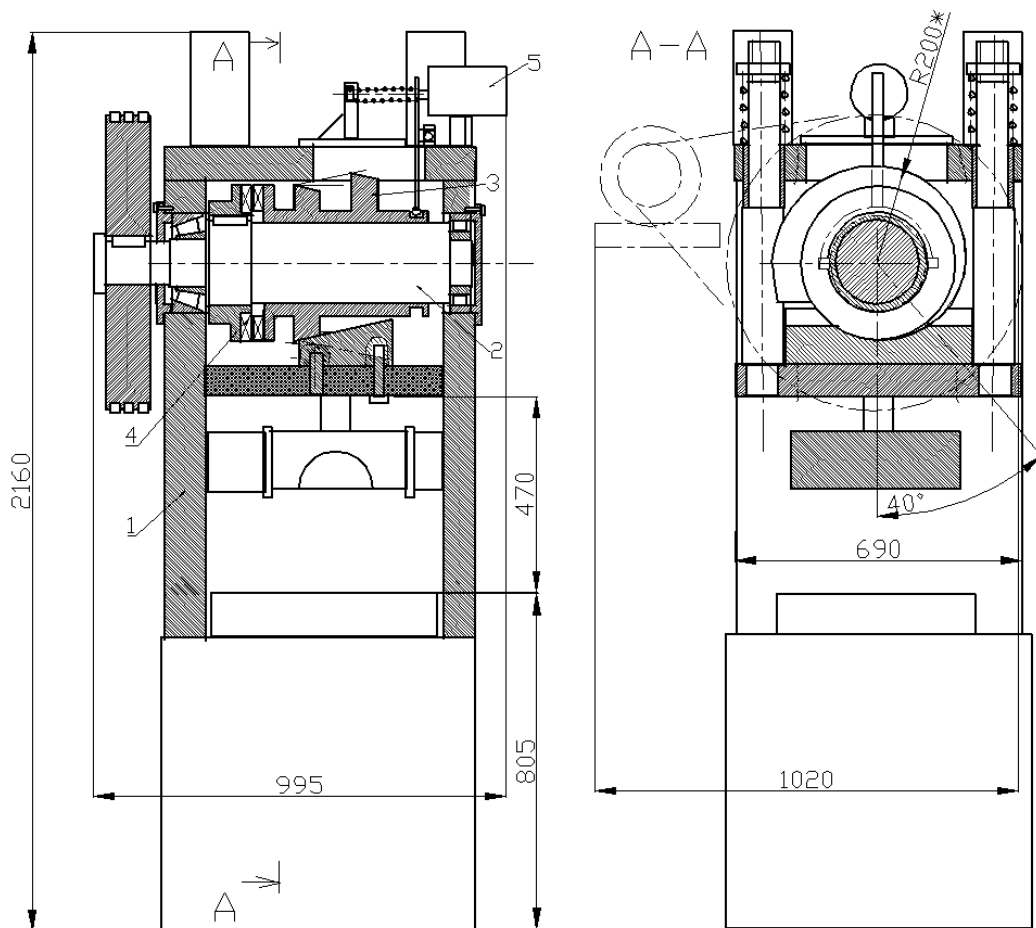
Общий вид пресса: 1 – корпус, 2 – вал, 3 – кулачково-винтовая поверхность, 4 – кулачковая муфта, 5 – электромагнитная катушка.
